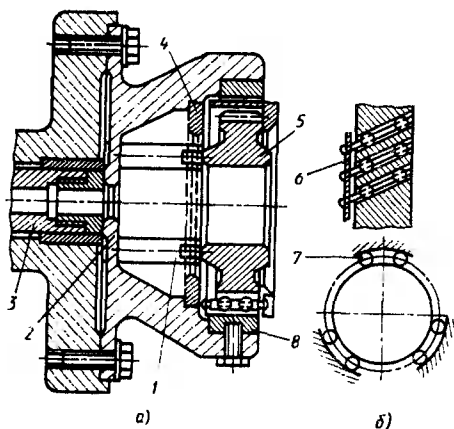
Мембранное приспособление для закрепления заготовки зубчатого колеса при шлифовании базового отверстия и торца: *a* — общий вид приспособления; *б* — сепаратор; 1 — опорные пальцы; 2 — мембрана; 3 — привод раскрытия патрона; 4 — съемное кольцо; 5 — за-
